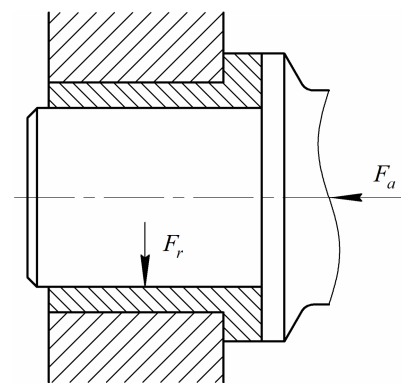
Радиально-упорный подшипник скольжения
